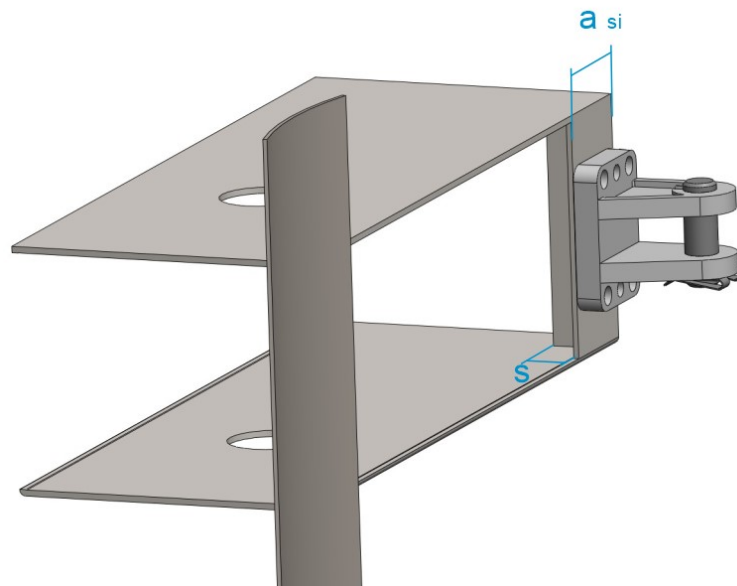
Dimensiones del soporte interno de la pieza móvil.
